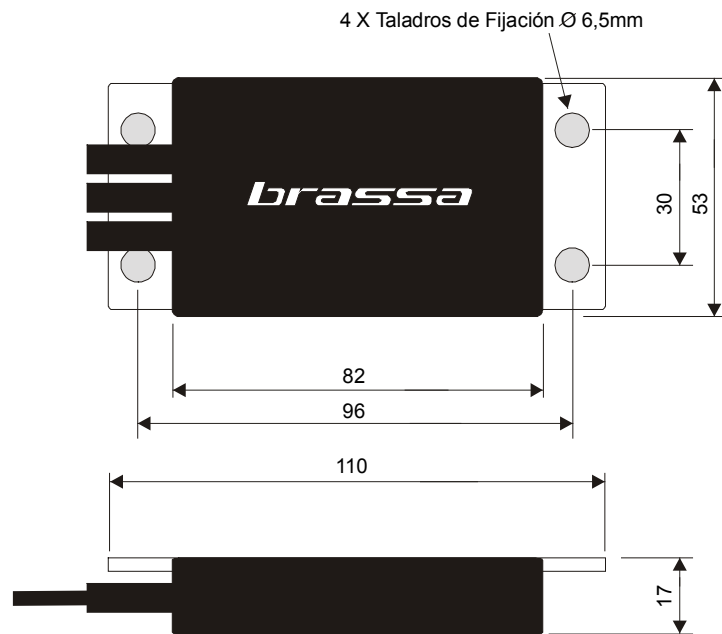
Dimensiones de la Unidad de Control CSPC-A
